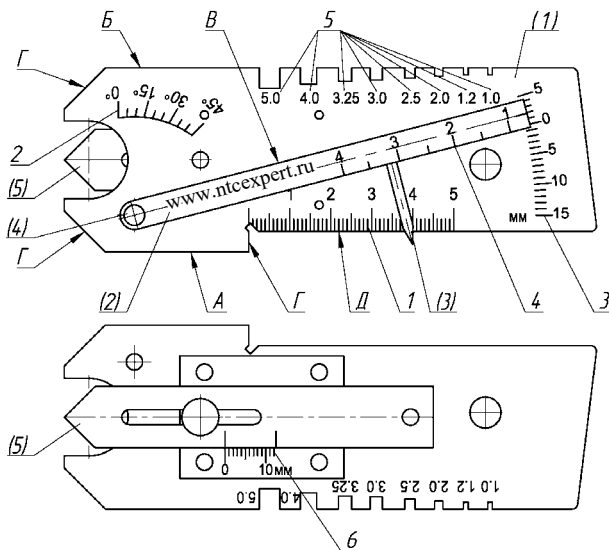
Универсальный шаблон сварщика «УШС-4».
